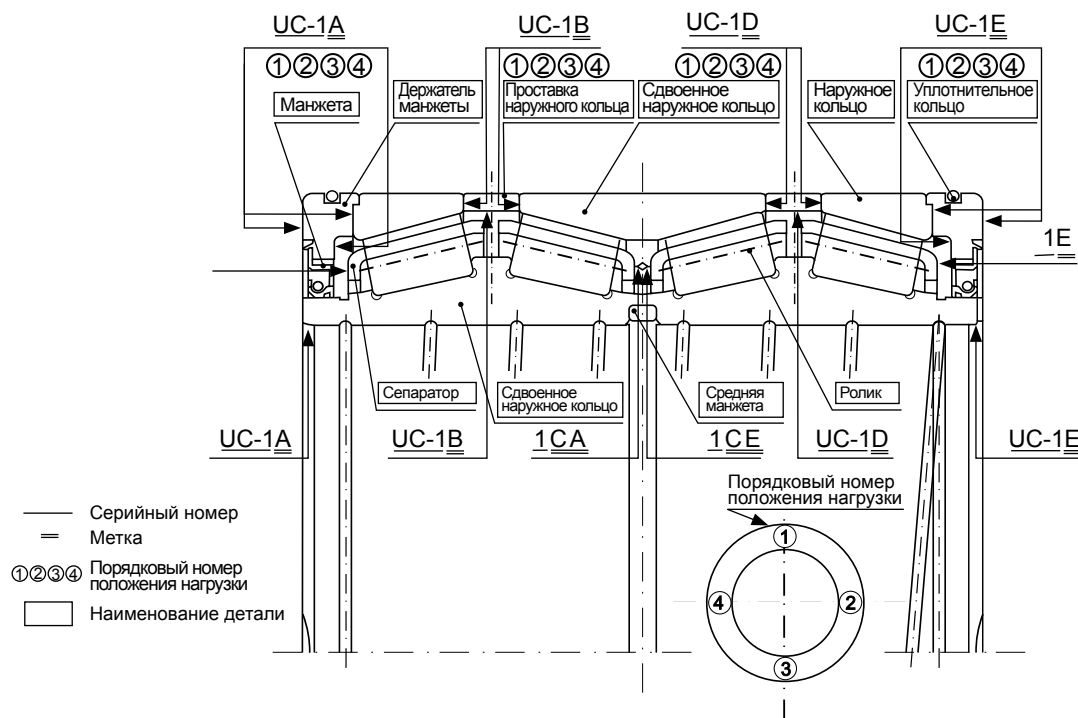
Наименование деталей и примеры маркировки (закрытые конические роликоподшипники).
